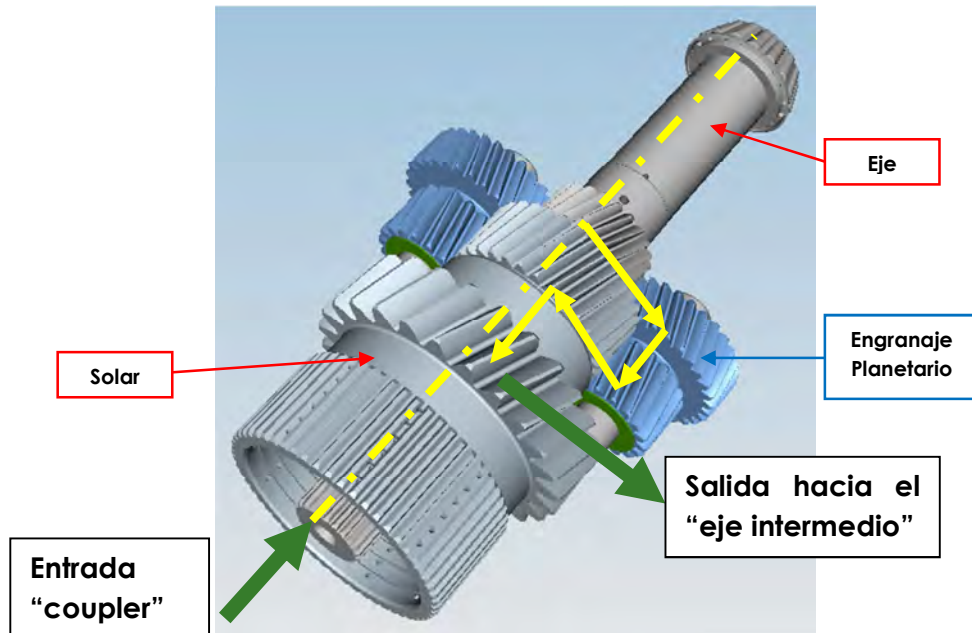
J GIRO DE LOS ENGRANAJES PLANETARIOS
